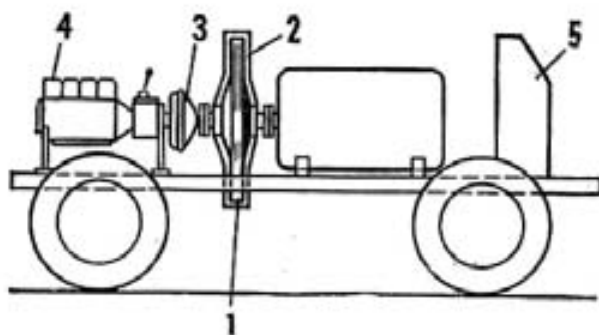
Маховичный генератор для сварки высоковольтной сети:
